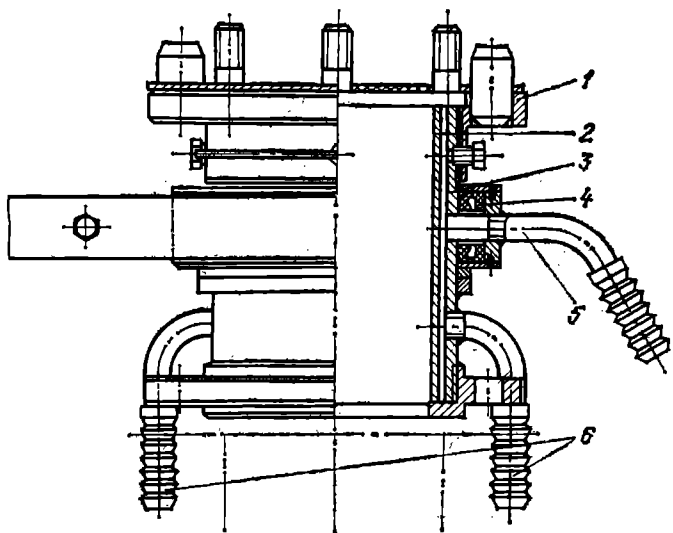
Переходный вертлюг-воздухораспределитель:
